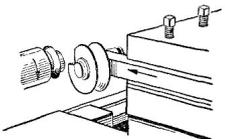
Установка и закрепление круглого фасонного резца в державке
